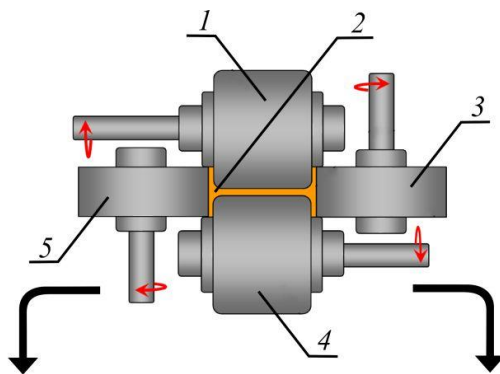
Рельсобалочный стан: 1, 3, 4, 5 – рабочие валки;
